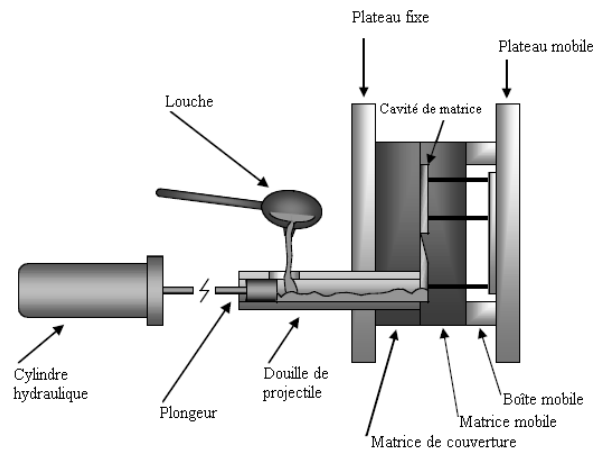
Machine de moulage mécanique sous pression avec chambre froide [1].
